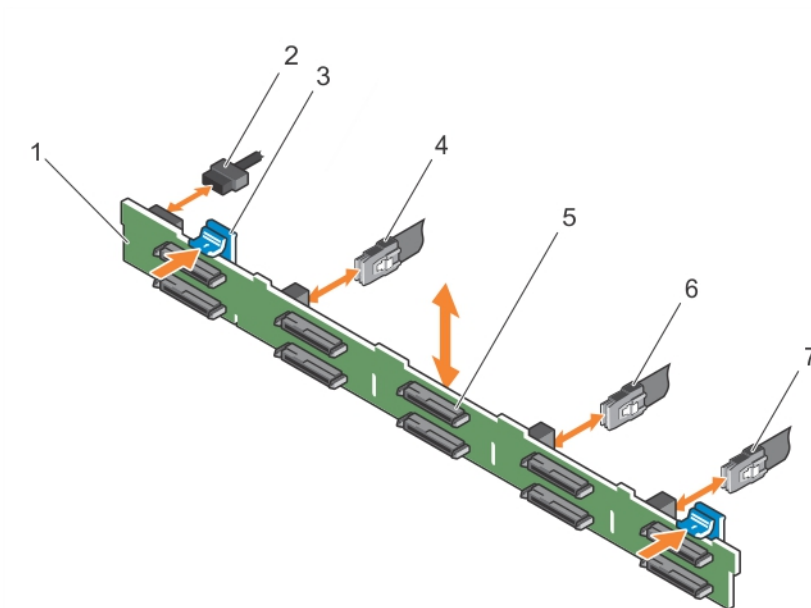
Extracción e instalación del plano posterior SAS/SATA (x10) de 2,5 pulgadas
